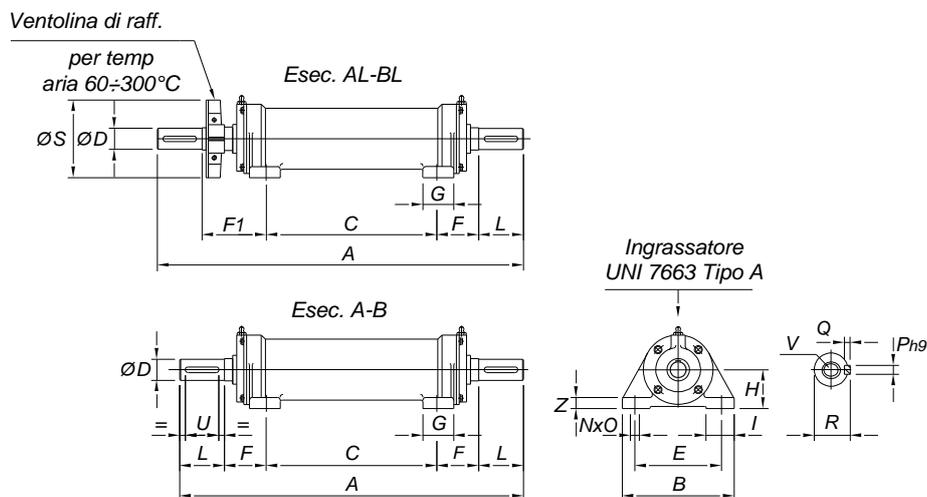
Supporti ST esecuzione A – AL – B – BL
